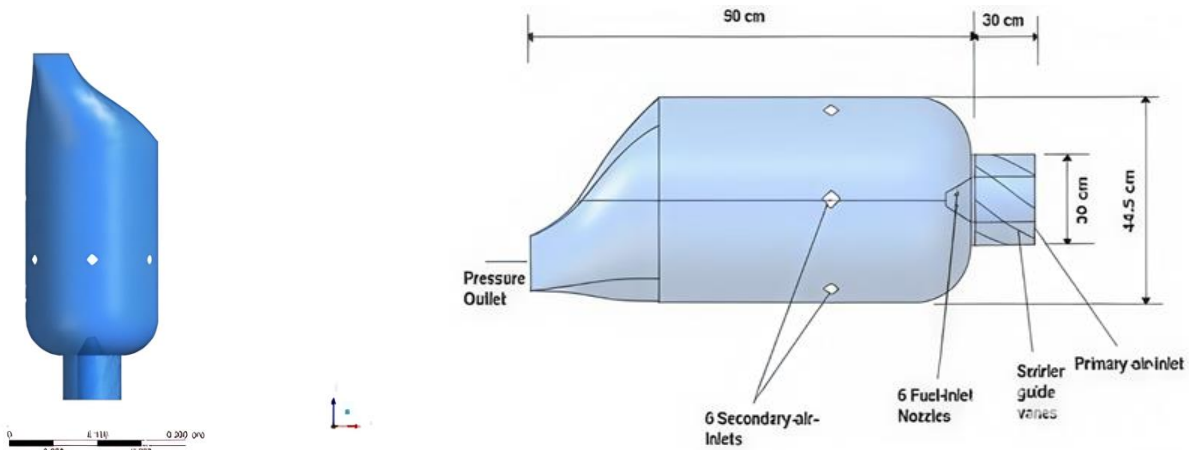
Vue d'ensemble de la géométrie schématiser et en 3D
